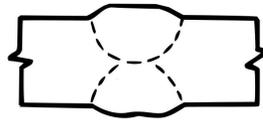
Perfil aceptable de soldadura a tope
